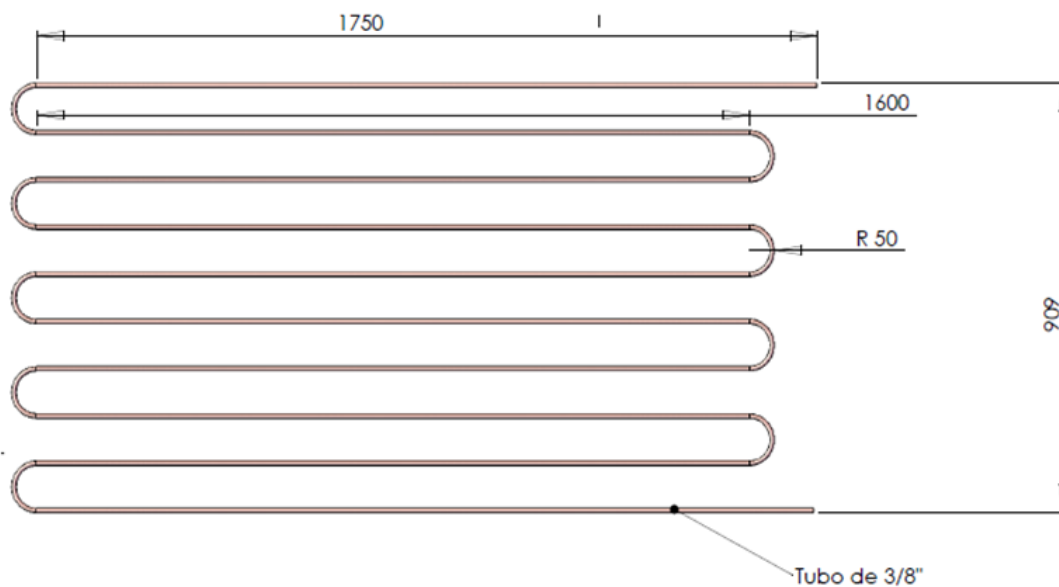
Desenho esquemático do evaporador solar.
